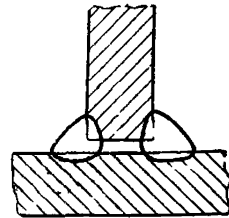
Сварное соединение тавровое без скоса кромок двустороннее
